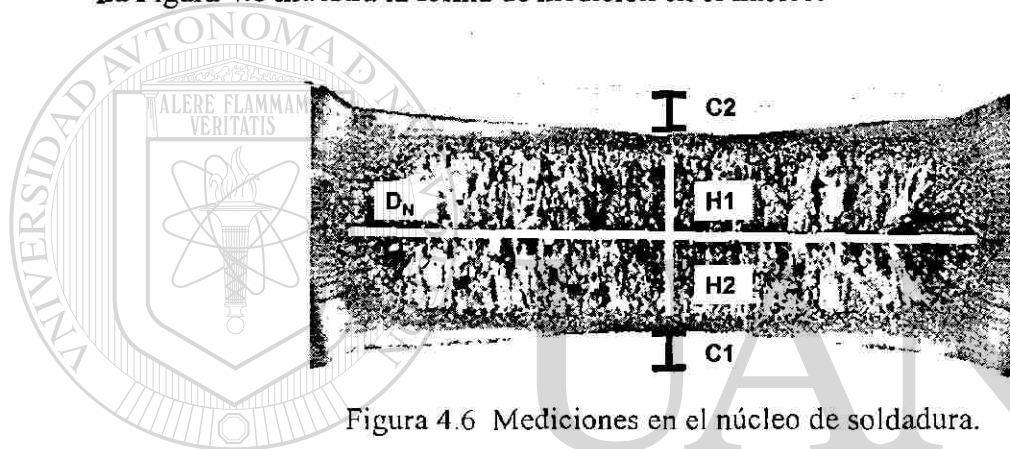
Mediciones en el núcleo de soldadura.
